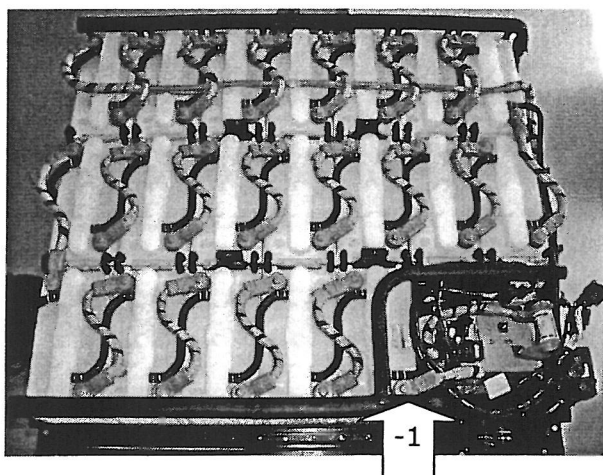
Ny HV boks (versjon E) komplett med nye kabler.
